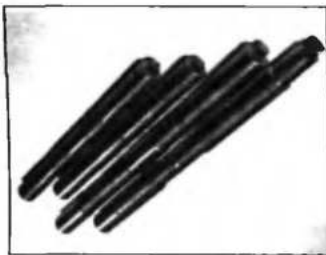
Набор борштанг с твердосплавными резцами для ремонта постелей распределительных валов в головках блоков цилиндров
